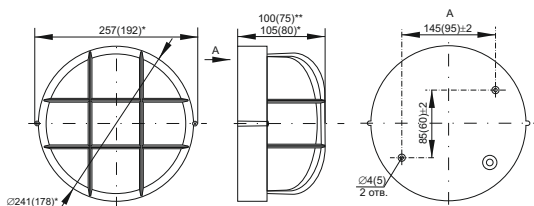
Габаритные и установочные размеры светильников НПП 1102, НПП1107
